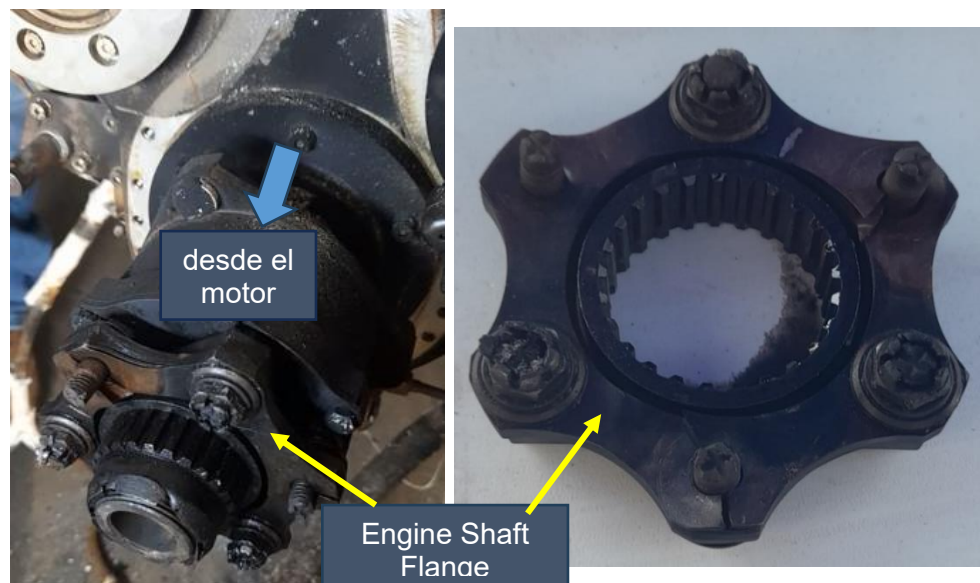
Vista de la conexión del eje con el Engine Shaft Flange.
